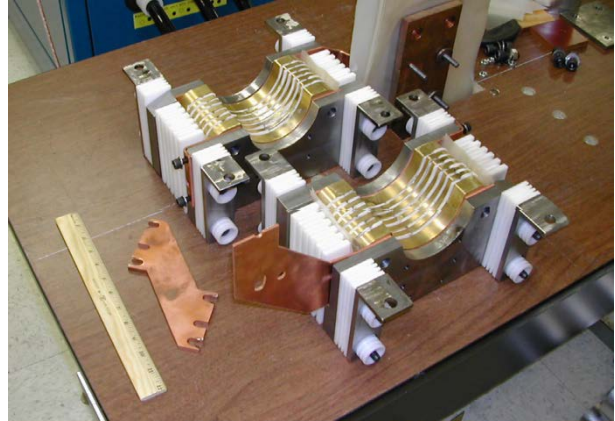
Atuador composto por duas metades para a moldagem tubos metálicos [37].
